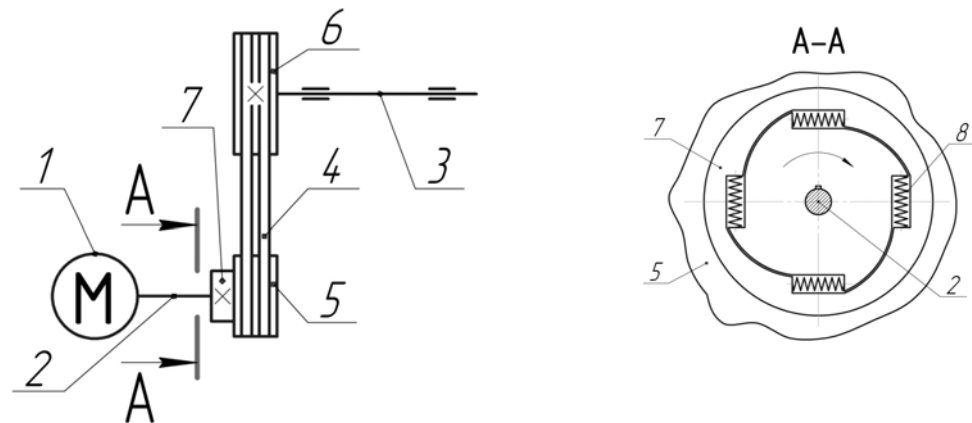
Кінематична схема привода основов'язальної машини з пружною муфтою з циліндричними пружинами стиску
